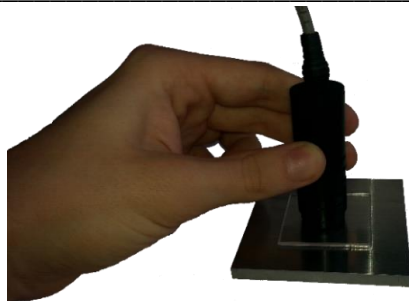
Установка преобразователя на образец с покрытия
